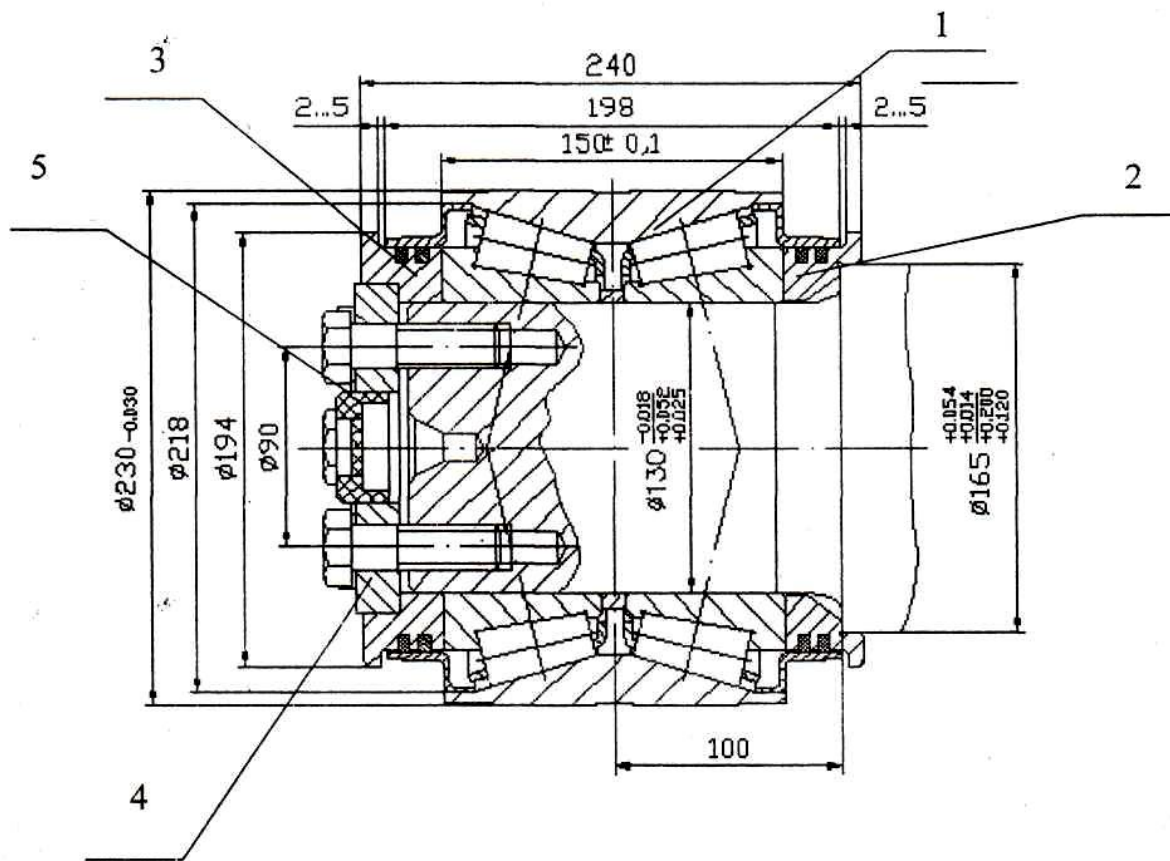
Буксовий вузол вантажного вагона з касетним конічним підшипником (без адаптера): 1 – дворядний касетний конічний підшипник ТВУ; 2 – задня кришка; 3 – передня кришка; 4 – торцева шайба; 5 – заглушка
